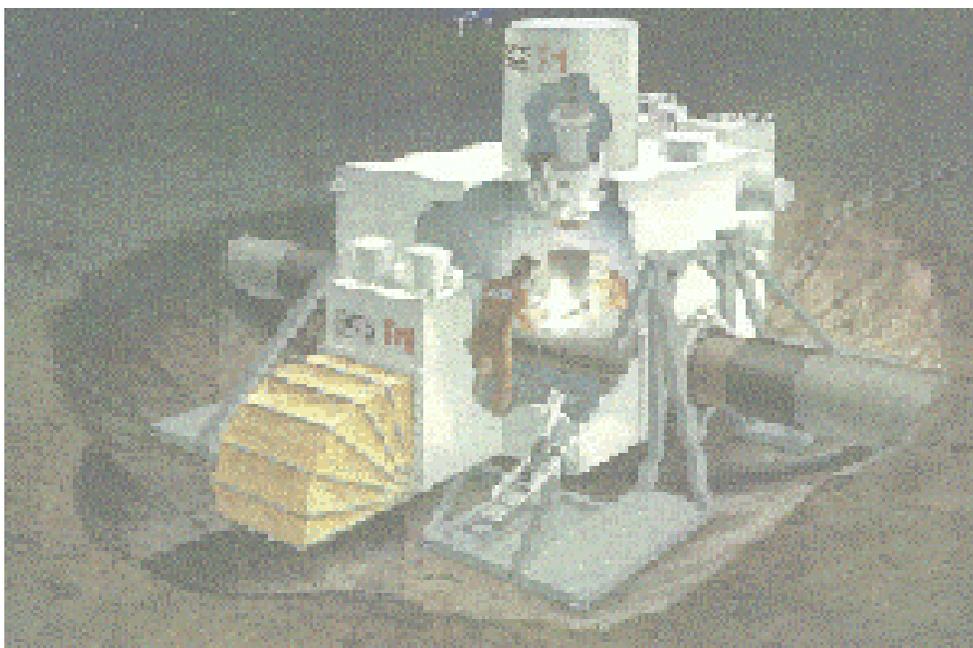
Hábitat seco con un soldador instalado sobre tubería sumergida para soldadura hiperbárica.
